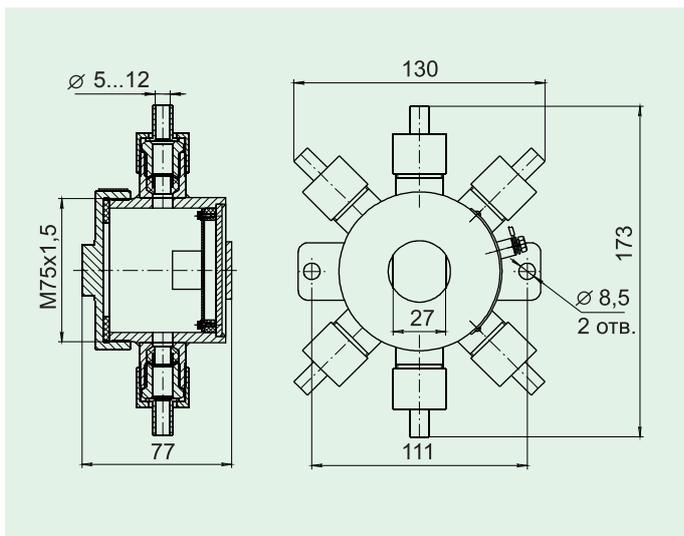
Коробка ВУУК. Габаритные и установочные размеры.
